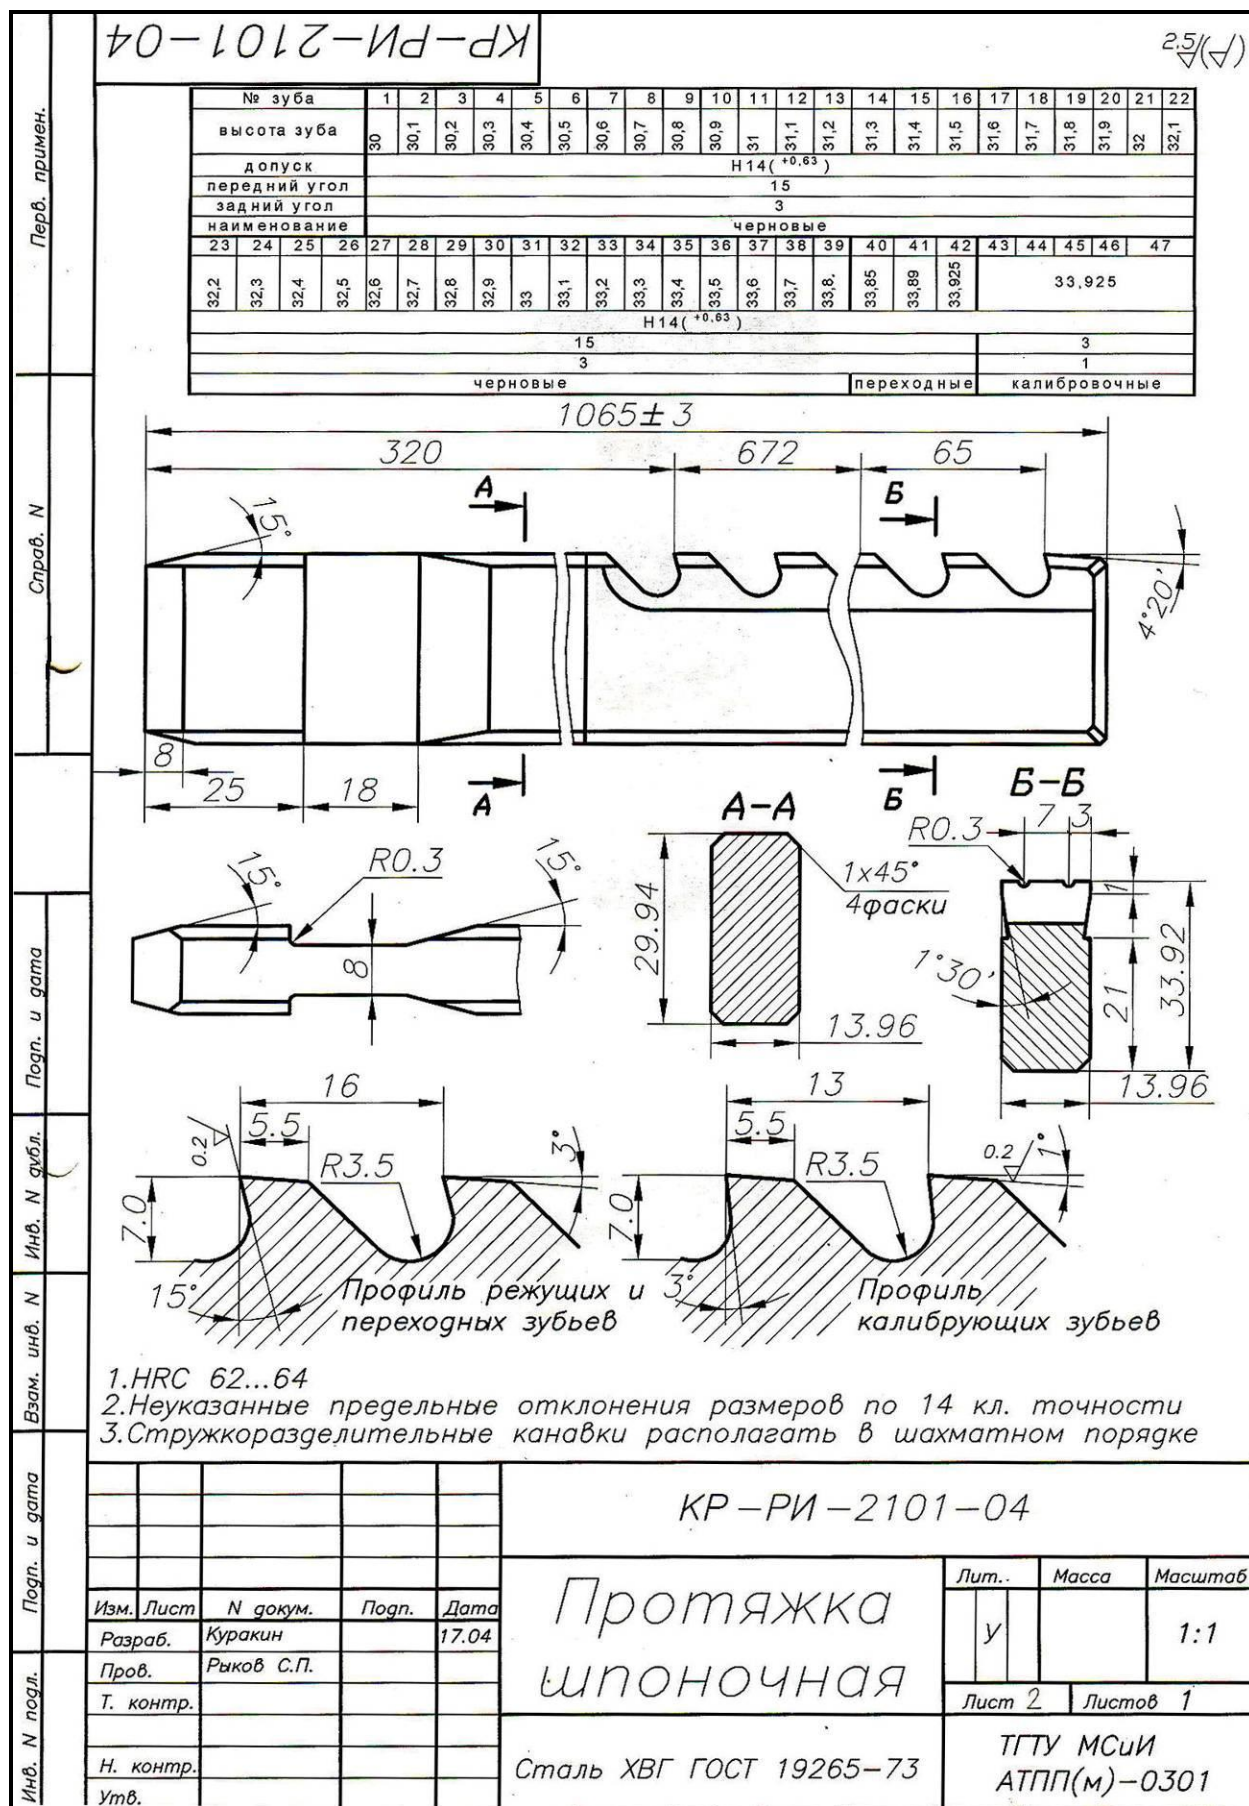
Рабочий чертеж шпоночной протяжки
